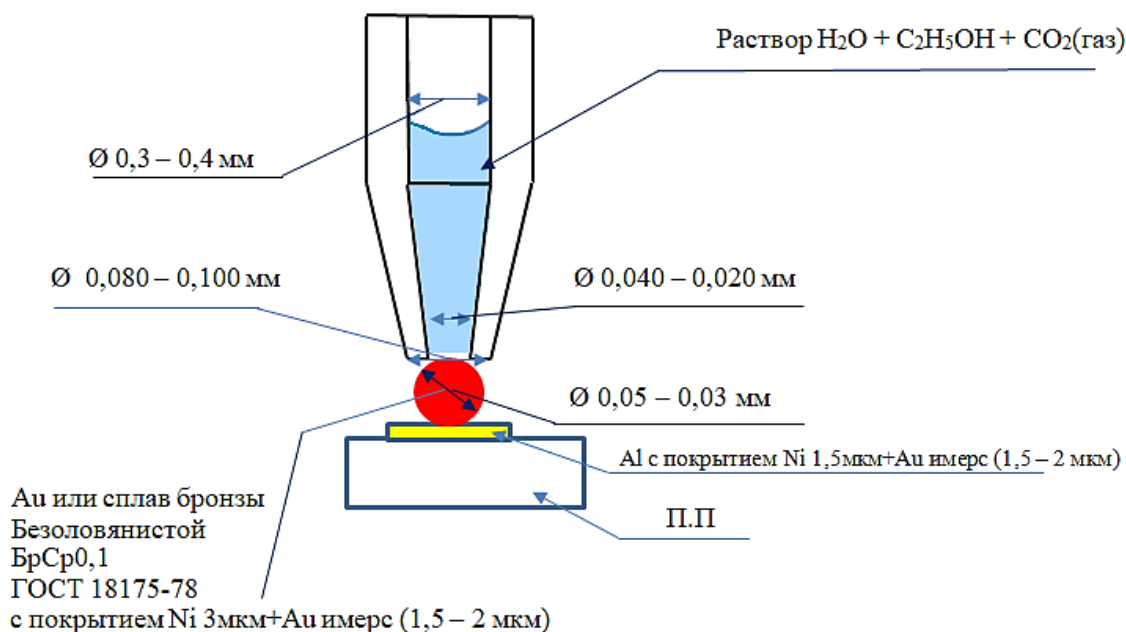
Элементарная схема кумулятивной сварки
